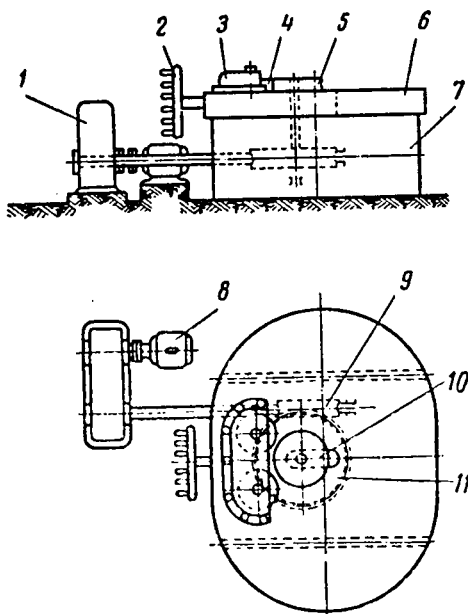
Схема роликового станка для гибки цилиндрического змеевика
